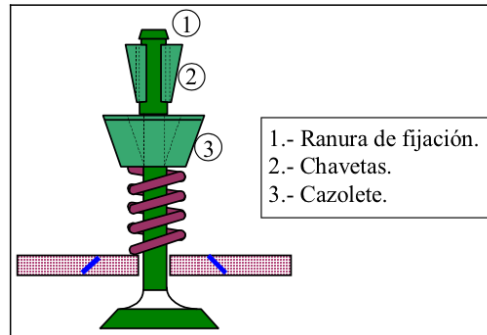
MONTAJE DE LA VÁLVULA Y DESPIECE DE SUS COMPONENTES
